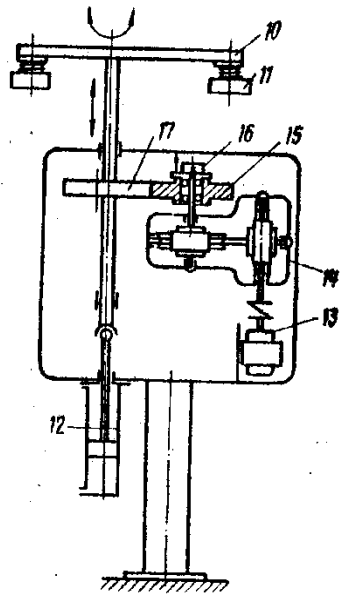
Схема механізму загрузки та вигрузки заготовок
